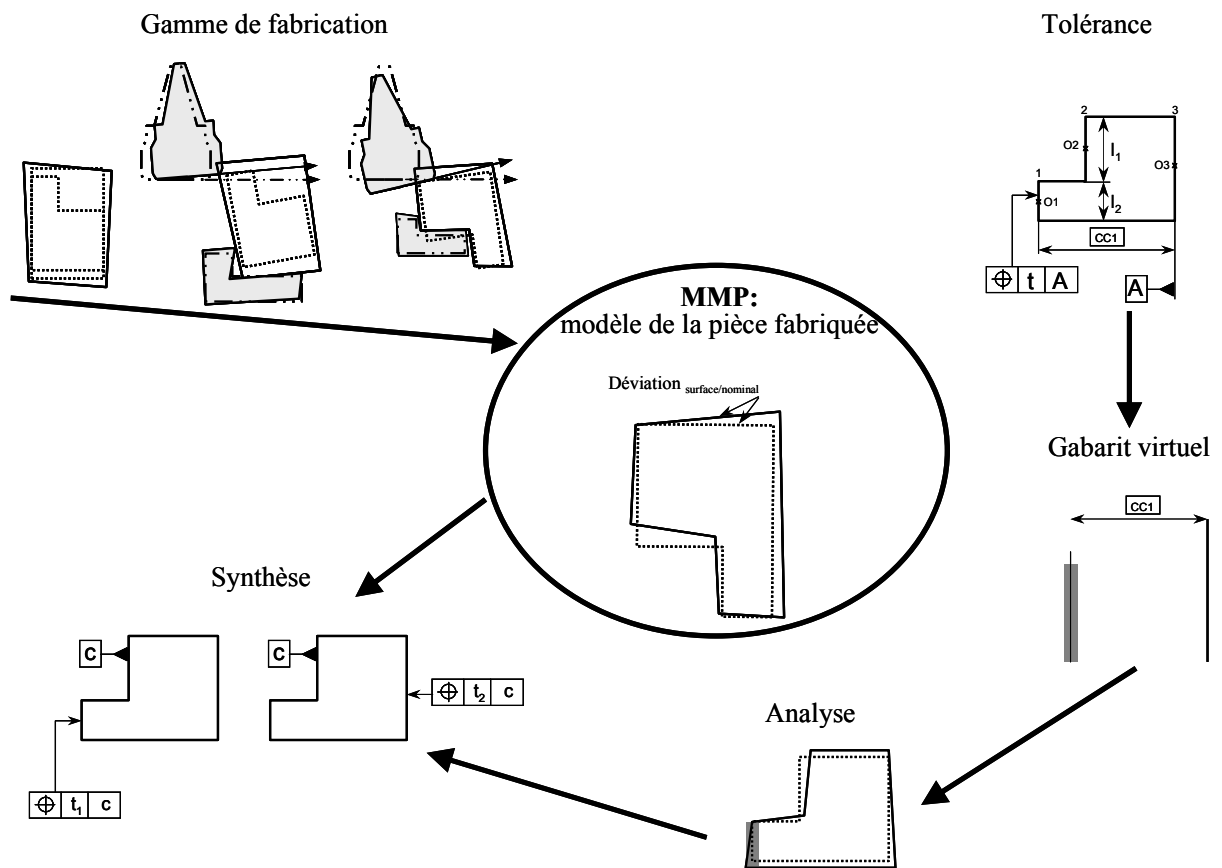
Vue générale de la méthode MMP [VIG 05]
